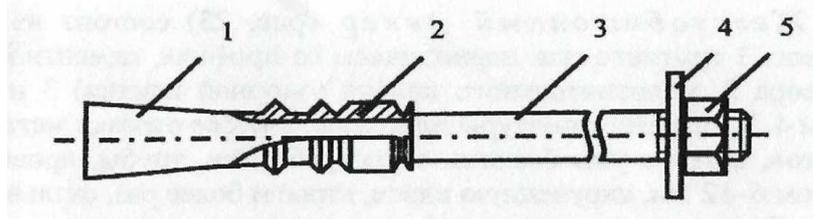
Конструкция металлического клинораспорного анкера ШК-1М
